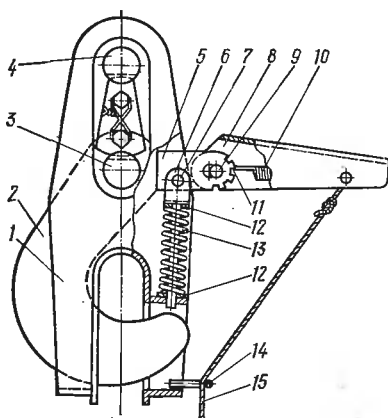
Полуавтоматический строповочный захват конструкции А. В. Загребельного:
